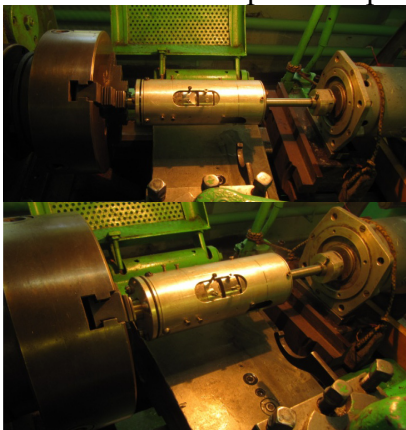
ШПФМ установленный в патроне токарного станка 1К62
